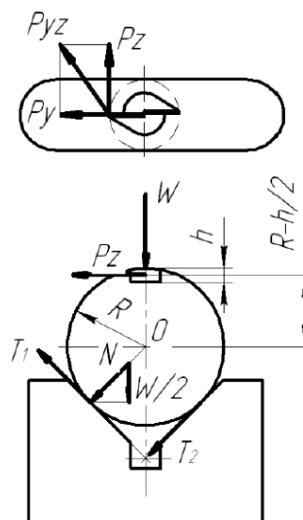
Схема сил при фрезеруванні шпонкового пазу
